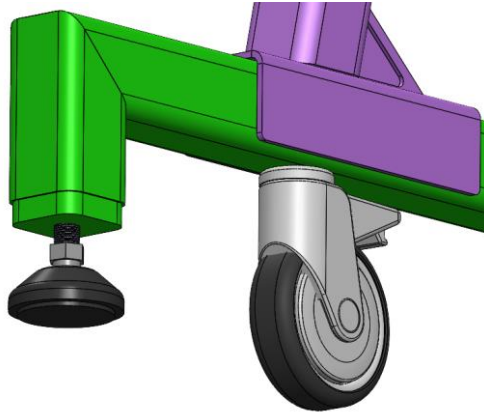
Vista detalle de la parte inferior (Fuente 22)
